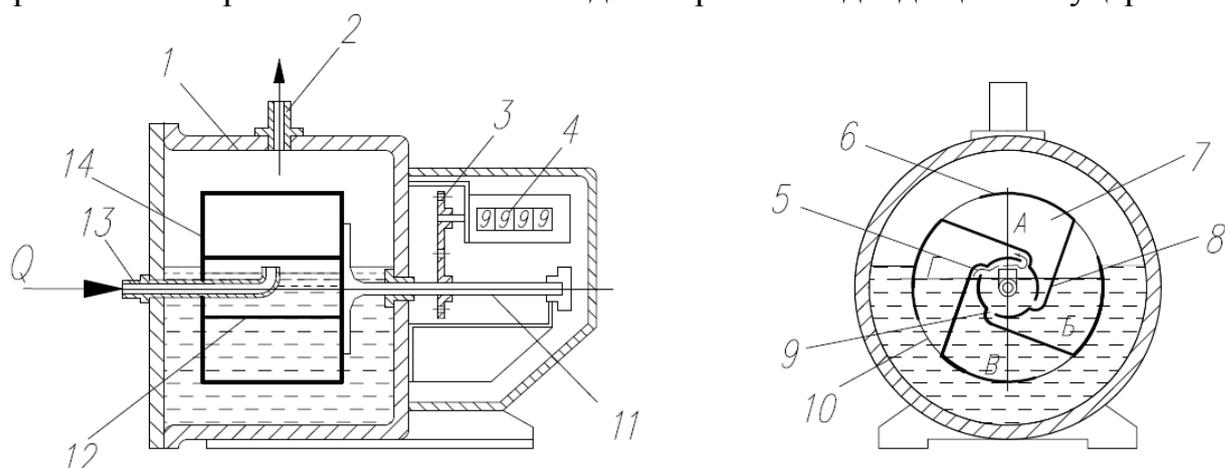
Принципиальная схема барабанного счетчика ГСБ-400: 1 — корпус; 2 — выходной штуцер; 3 — редуктор; 4 — счетчик оборотов; 5 — отверстия для выхода газа; 6 — наружная обечайка; 7 — измерительная камера; 8 — перегородка; 9 — входное отверстие камеры; 10 — выходное отверстие камеры; 11 — ось барабана; 12 — внутренний цилиндр барабана; 13 — входной штуцер; 14 — барабан;
